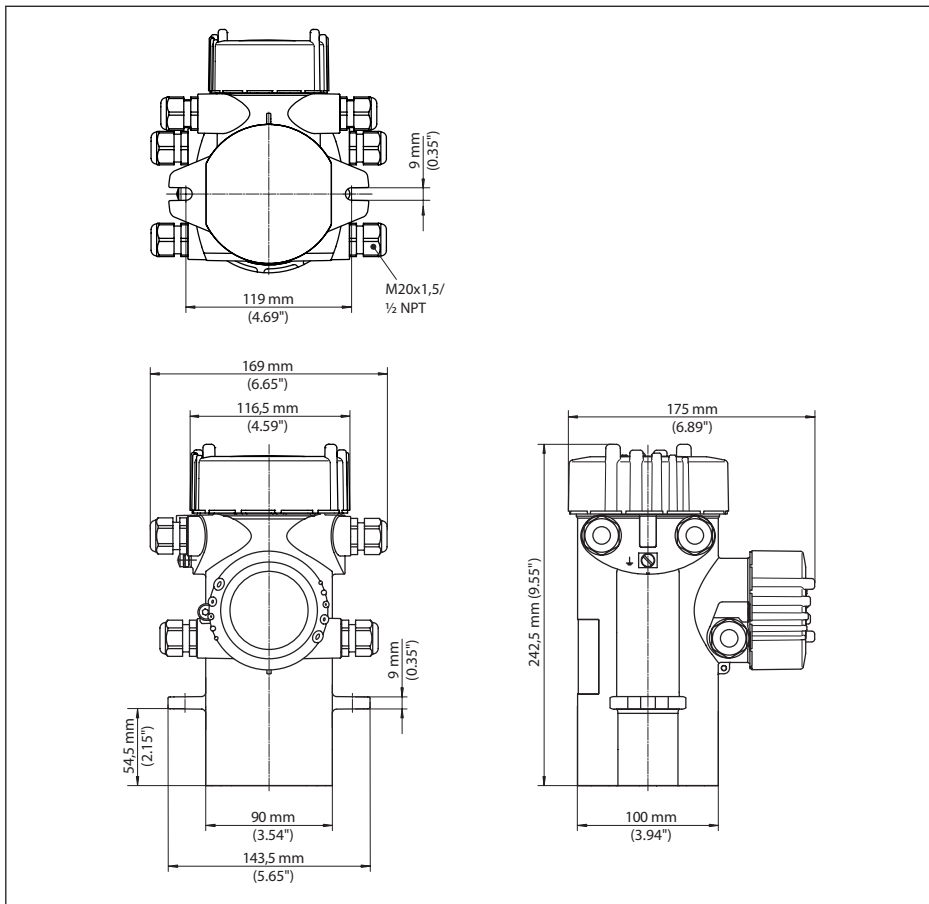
Aluminiumgehäuse bzw. Edelstahlgehäuse - Feinguss
